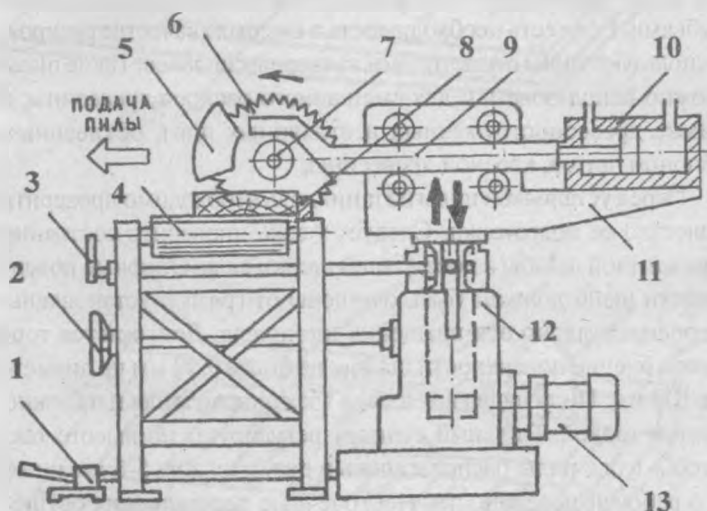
Станок торцовочный с прямолинейным движением пилы: 1-педаль; 2-маховичок подъема колонки; 3-рукоятка зажима колонки; 4-стол с роликами; 5-ограждение; 6-пила; 7-электродвигатель; 8-направляющая линейка; 9-суппорт; 10-гидроцилиндр; 11-колонка; 12-станина; 13-электродвигатель гидропривода подачи
